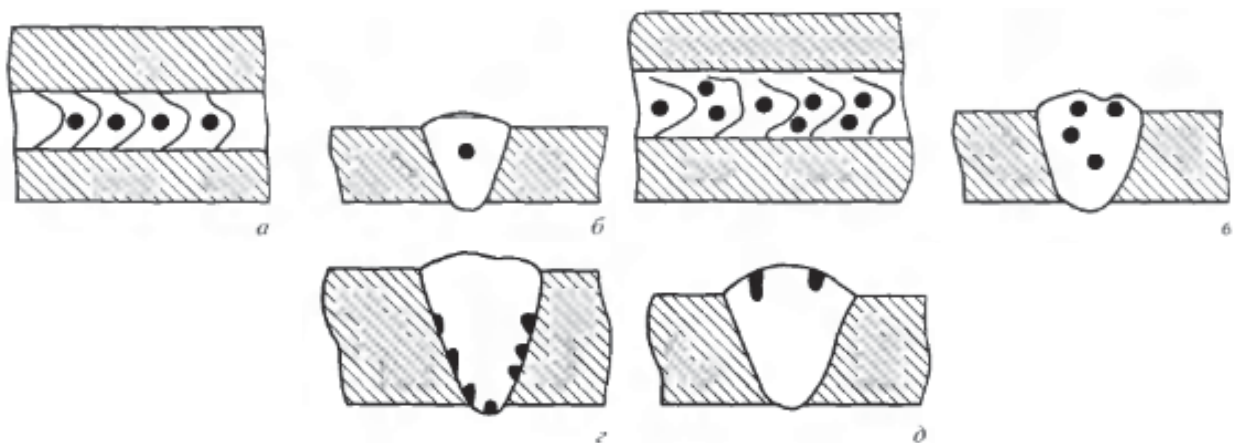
Схематичное изображение поры сварного соединения
